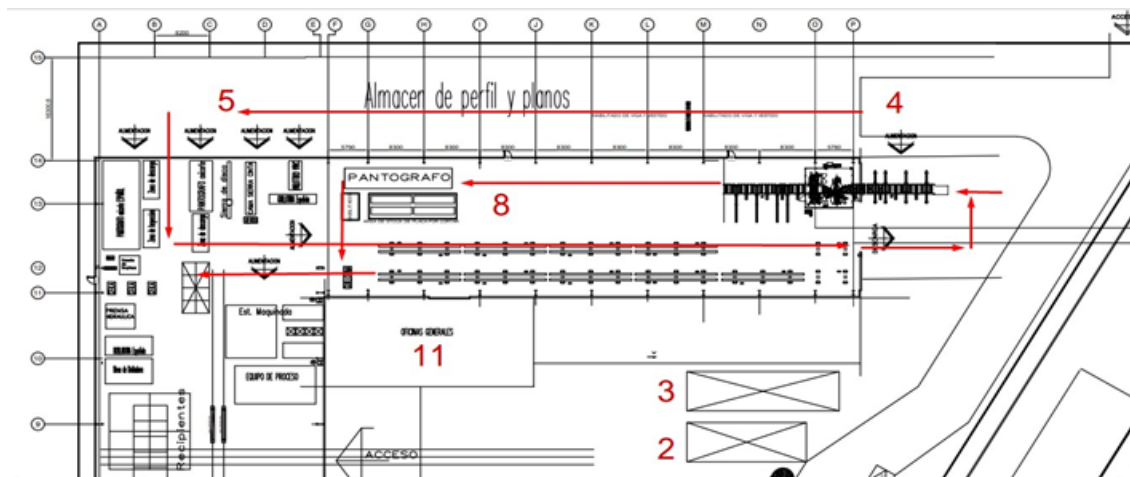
Layout prueba 3 de la Planta Durosa Santa Rosa SA, de CV.
